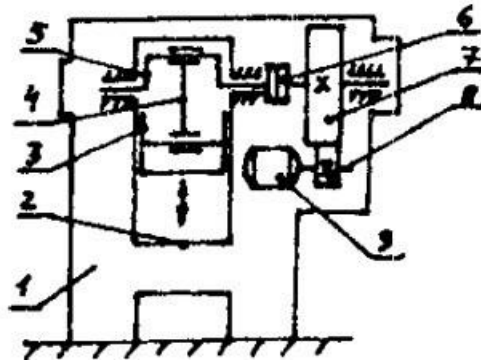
Схема кривошипного пресса: 1 - станина; 2 - стол пресса; 3 - ползун; 4 - шатун; 5 - коленчатый вал; 6 - соединительная муфта; 7 - маховик; 8 - шестерня; 9 - электродвигатель
